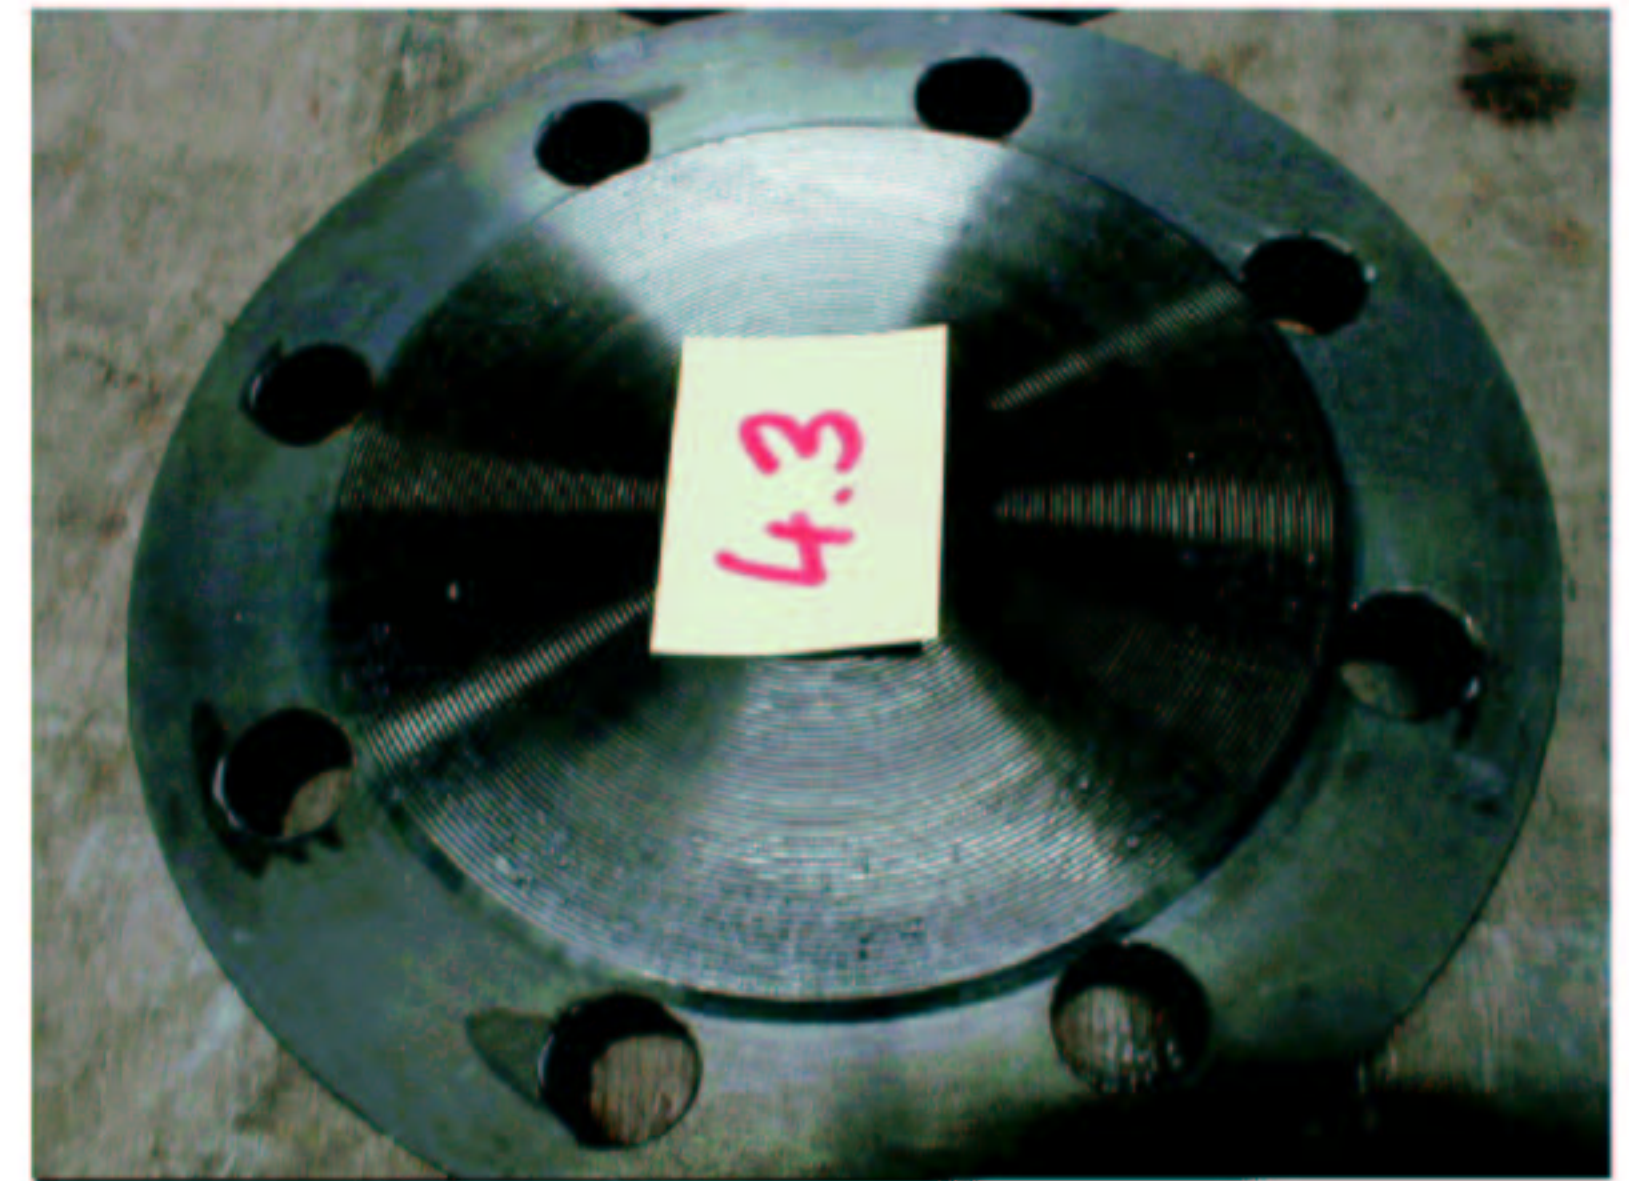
Geringe Anhaftungen am Flansch nach gelöster Dichtung
